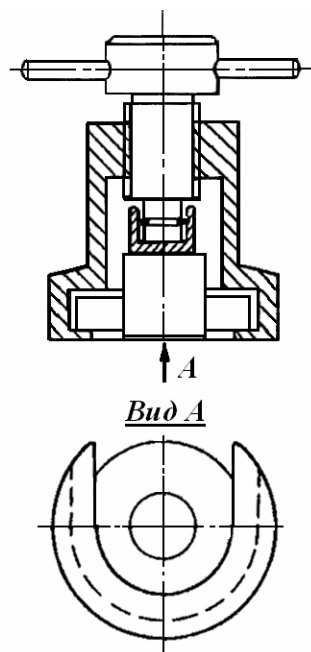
Винтовой упорный съемник с захватом детали корпусом съемника
